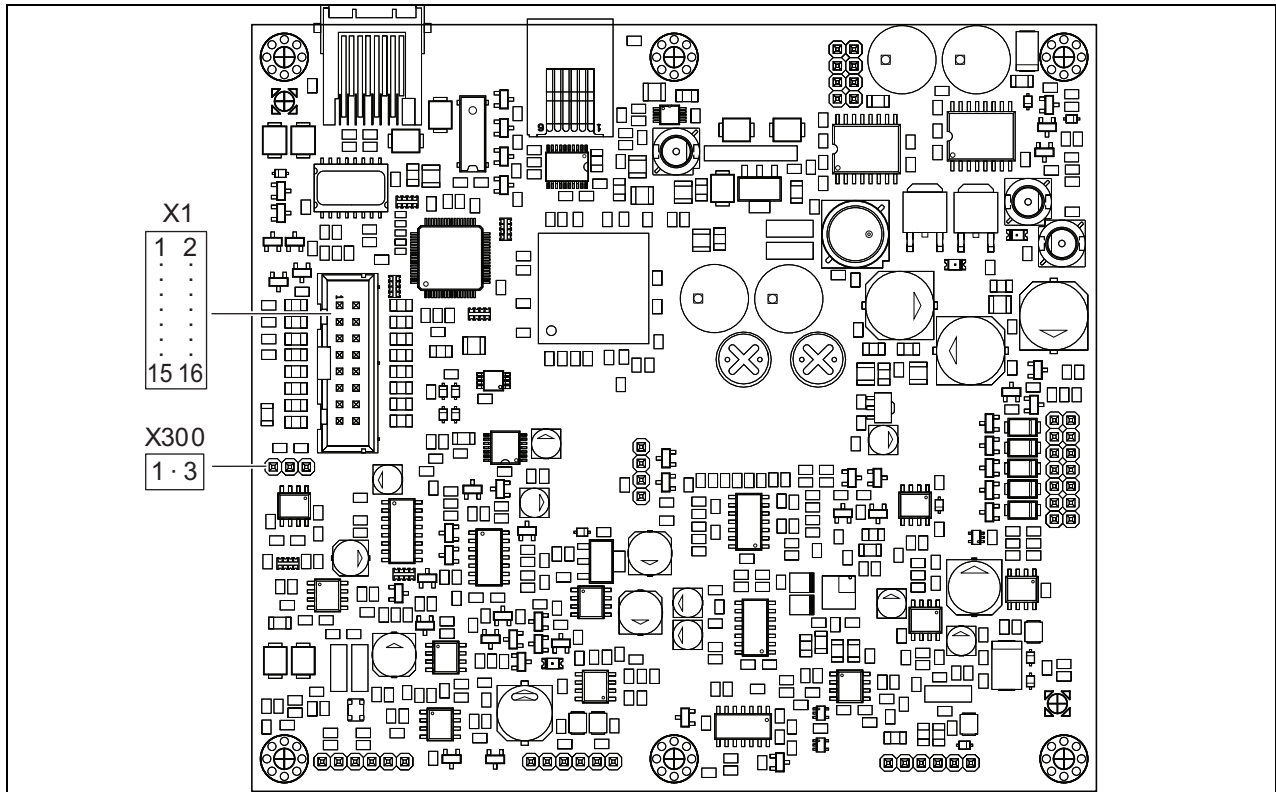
PRS-CSRМ 구성부품 측면 PCB
